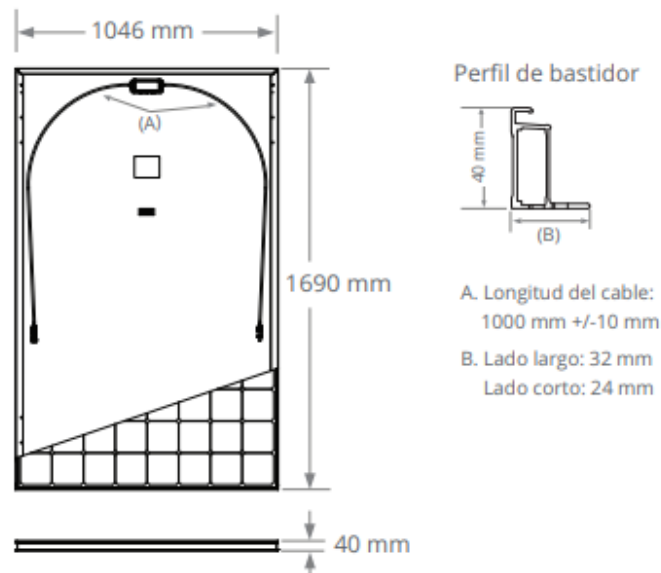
Dimensiones panel fotovoltaico (Ficha técnica)
